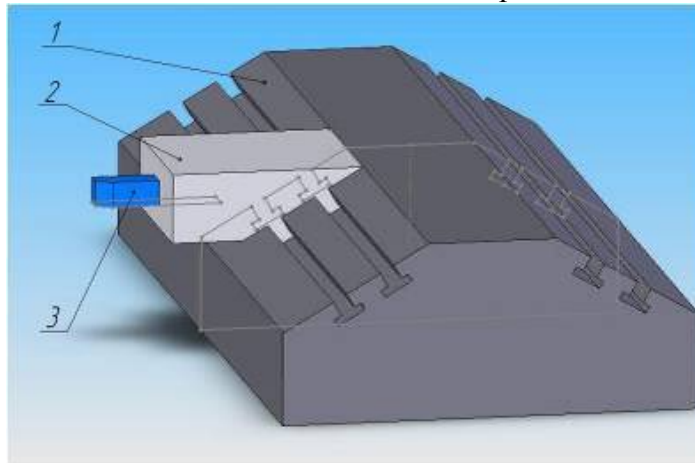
Инструментальный комплекс станка ПАБ-160.
